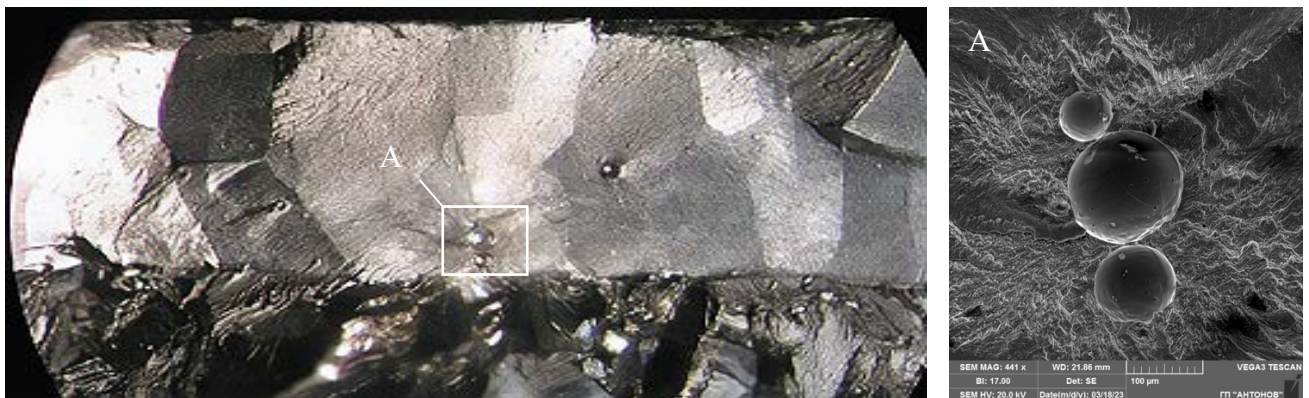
Пори в наплавлені шарі, зразок зі сплаву ВТ22
